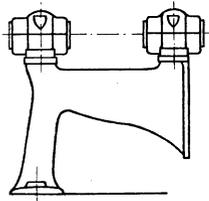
Exhaustorbock mit aufgesetzten Lagern.
